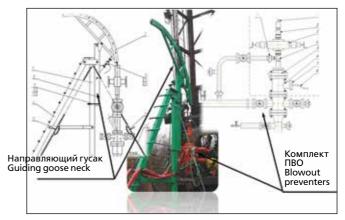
Устьевое оборудование Figure 3 - Wellbead equipment
